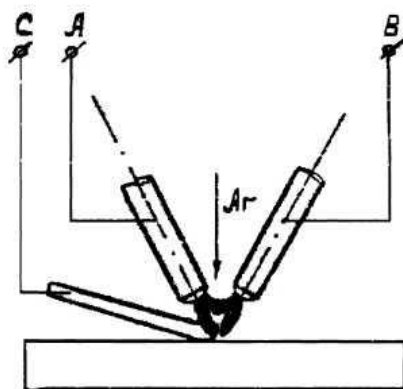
Сварка трехфазной дугой с применением регулировки необходимого тепловложения
